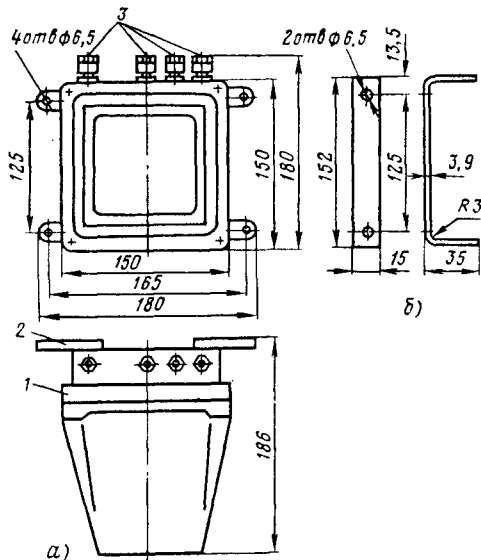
Общий вид и габаритные размеры регуляторов пневматических Р-1, Р-2:
